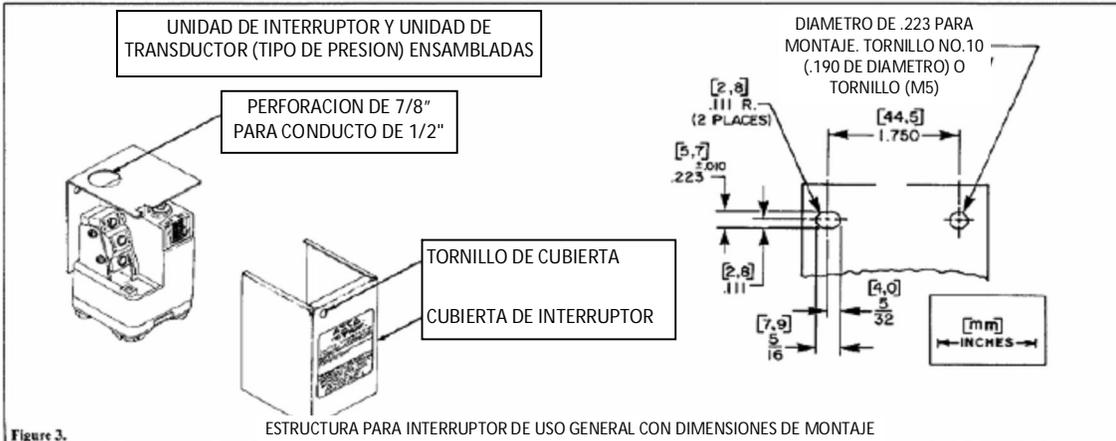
ESTRUCTURA PARA INTERRUPTOR DE USO GENERAL CON DIMENSIONES DE MONTAJE
